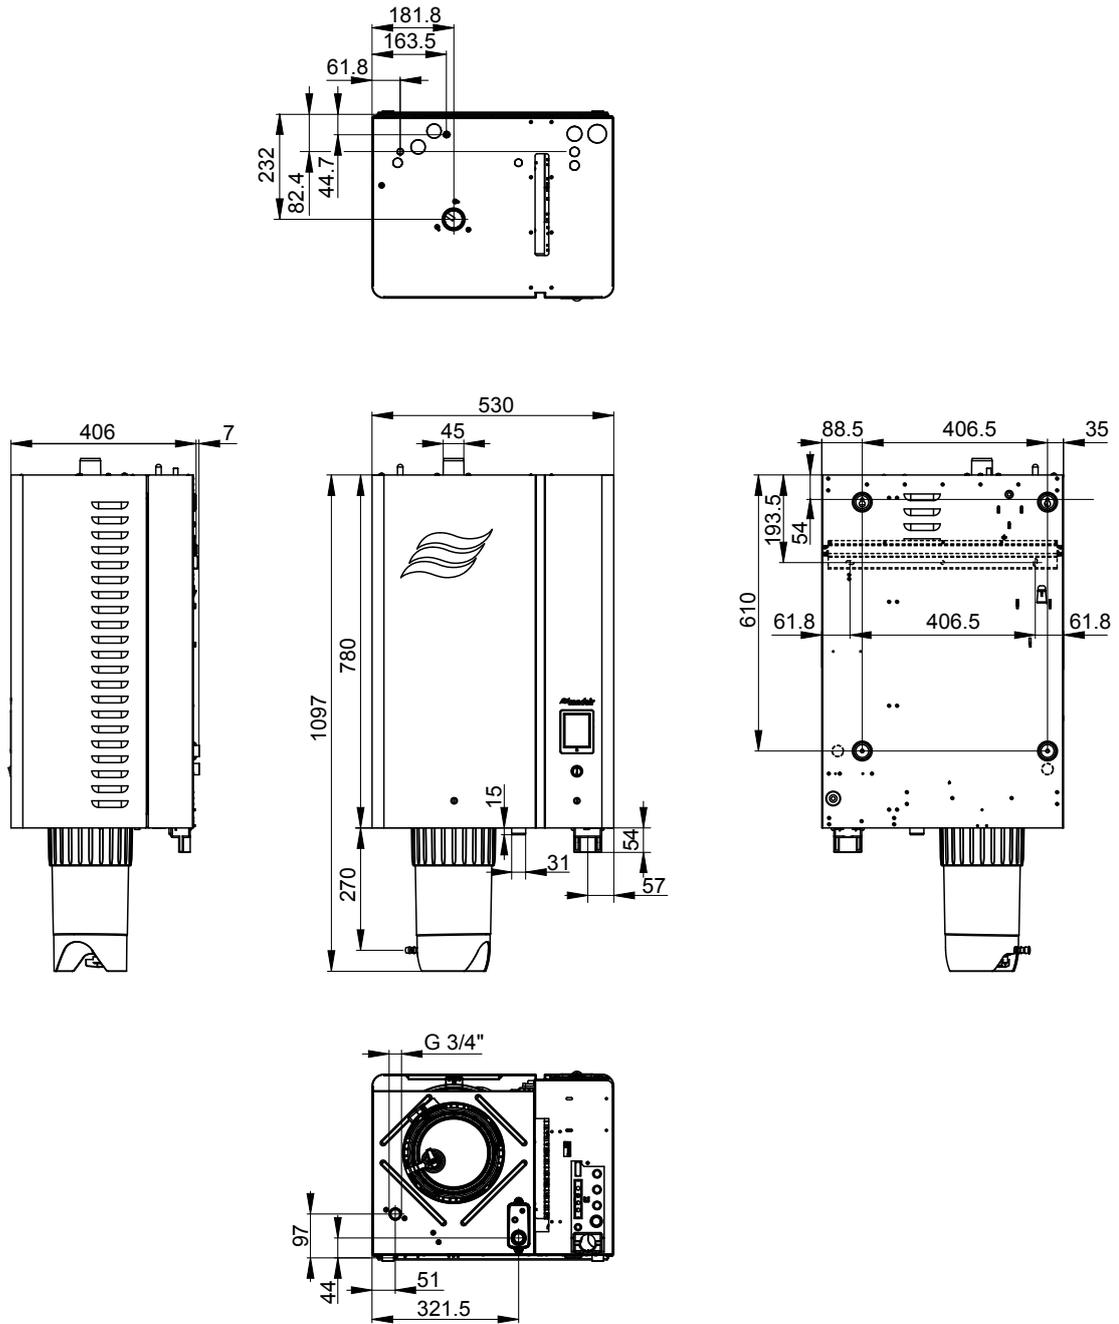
Figura de dimensiones del equipo "M" (dimensiones en mm)
